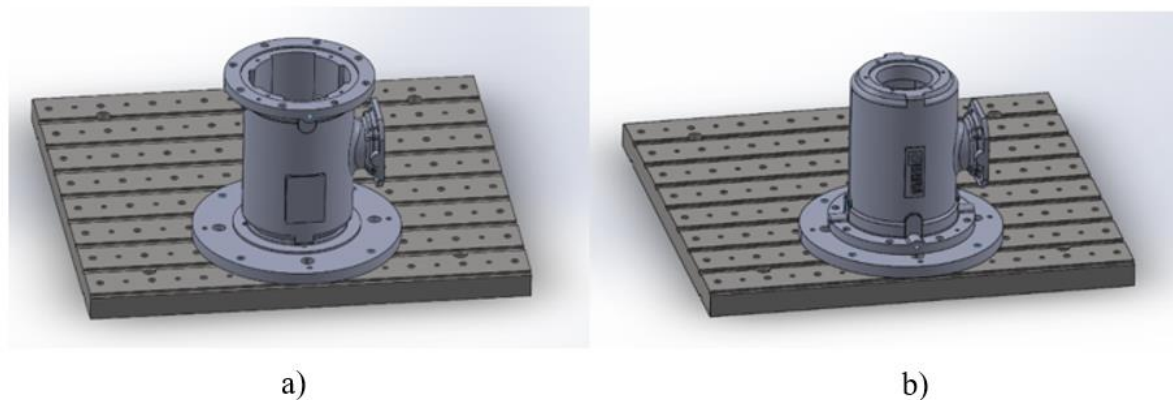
Fixações da carcaça através do prato: a) Primeira fase de maquinagem; b) Segunda fase de maquinagem.
